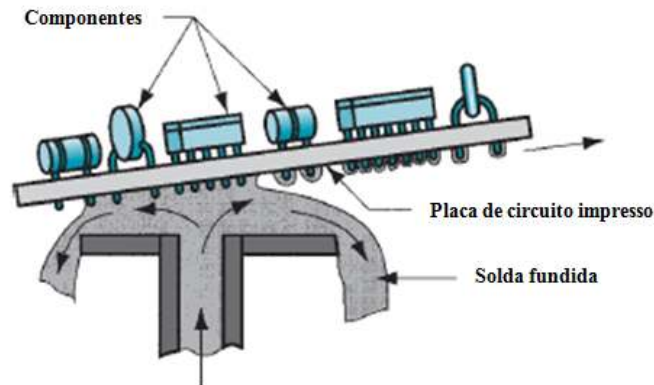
Representação do processo de soldagem *Wave*. Adaptado de [7].
